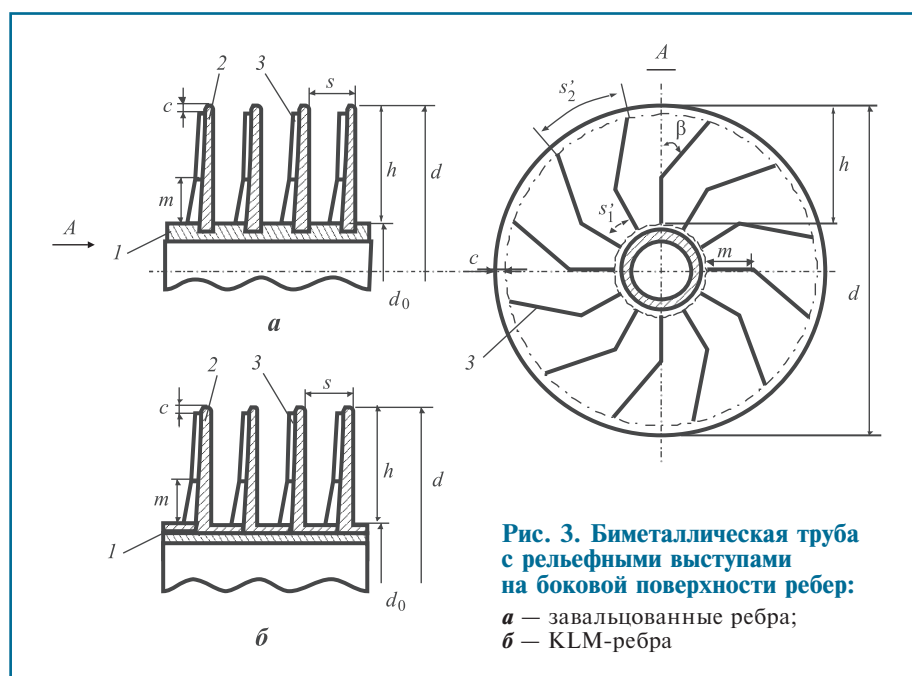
Биметаллическая труба с рельефными выступами на боковой поверхности ребер:
